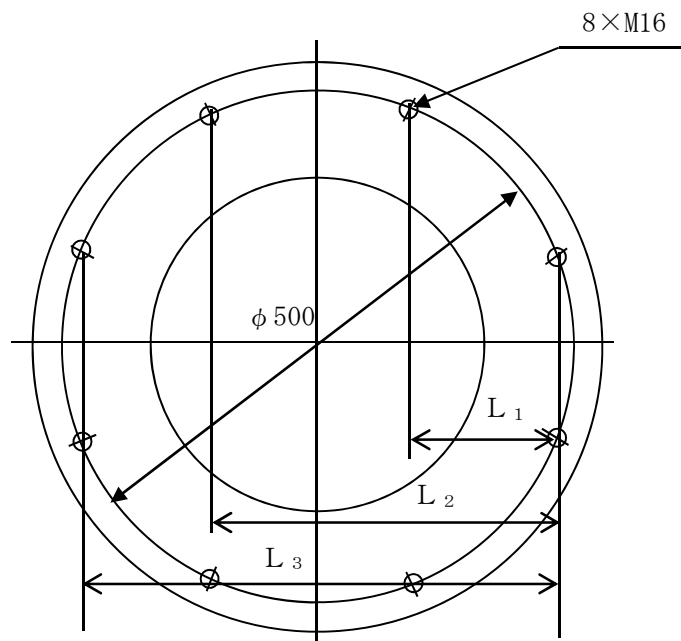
原動機取付ボルトの各ボルト間寸法の配置図
